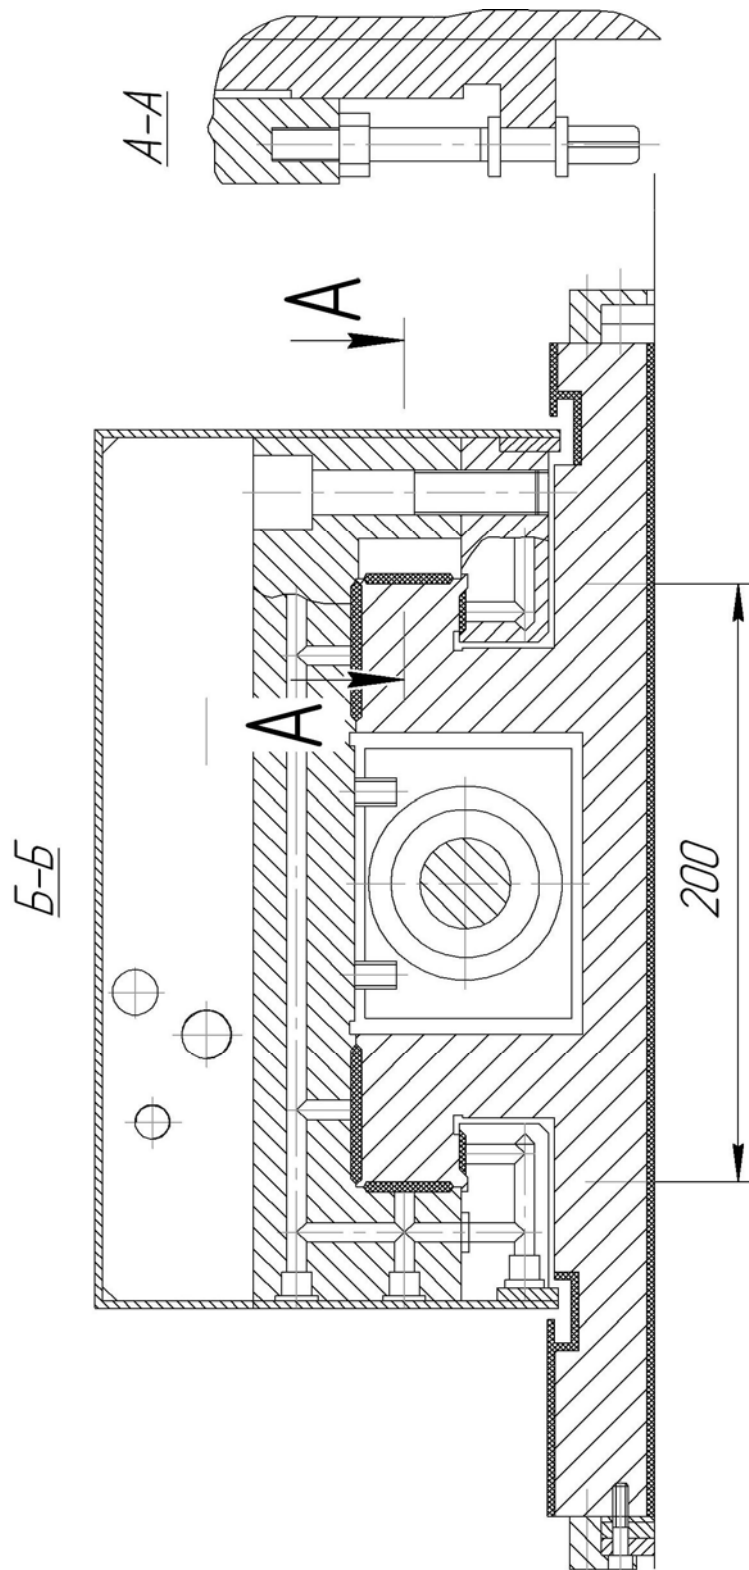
Пояснить основные особенности направляющих токарного станка с ЧПУ
